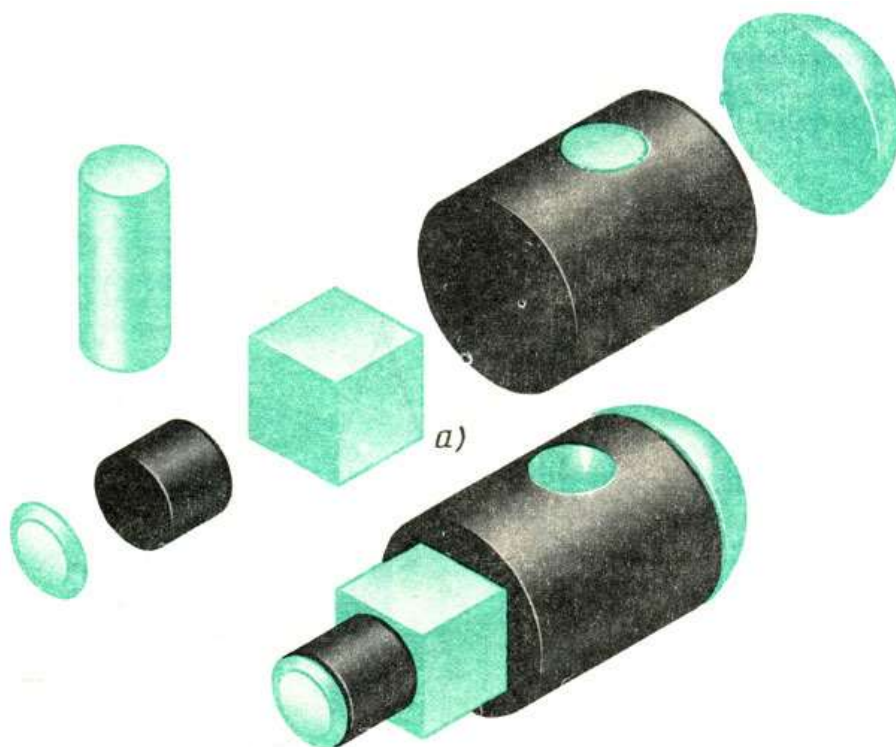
Анализ геометрической формы заготовки ключа: а - элементы детали; б - общий вид детали
